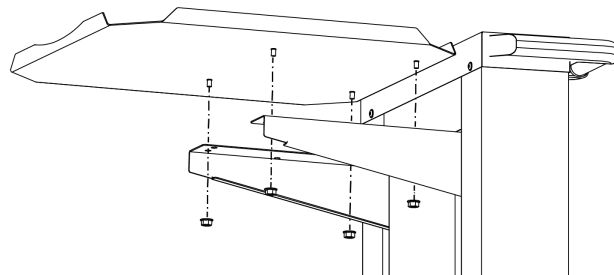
Montage de la plateforme pour paniers ou plateaux
